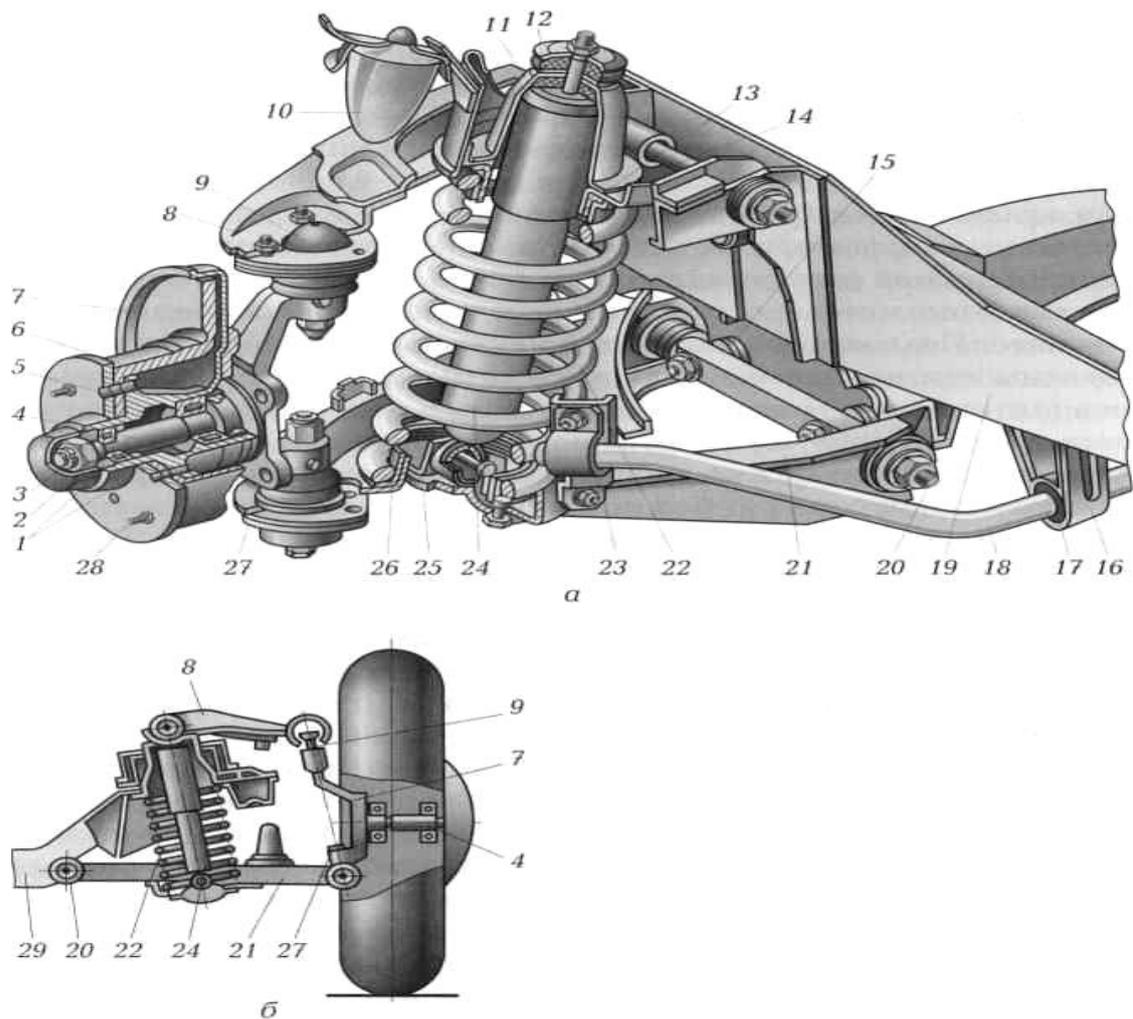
Устройство [а] и типовая схема (б) передней подвески автомобилей ВАЗ классической компоновки:
